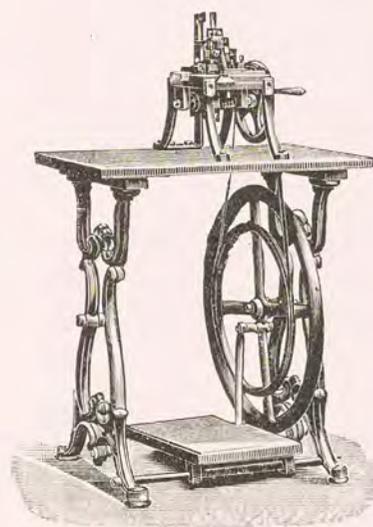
Automatische Einhängemaschine für Fuchsschwanzketten.
